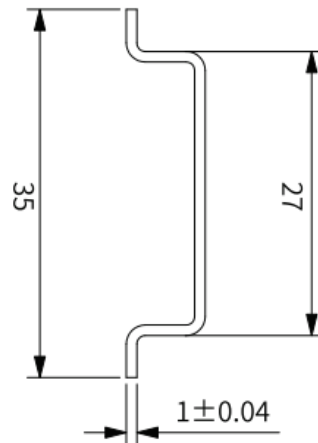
Размер DIN-рейки по стандарту МЭК-60715
